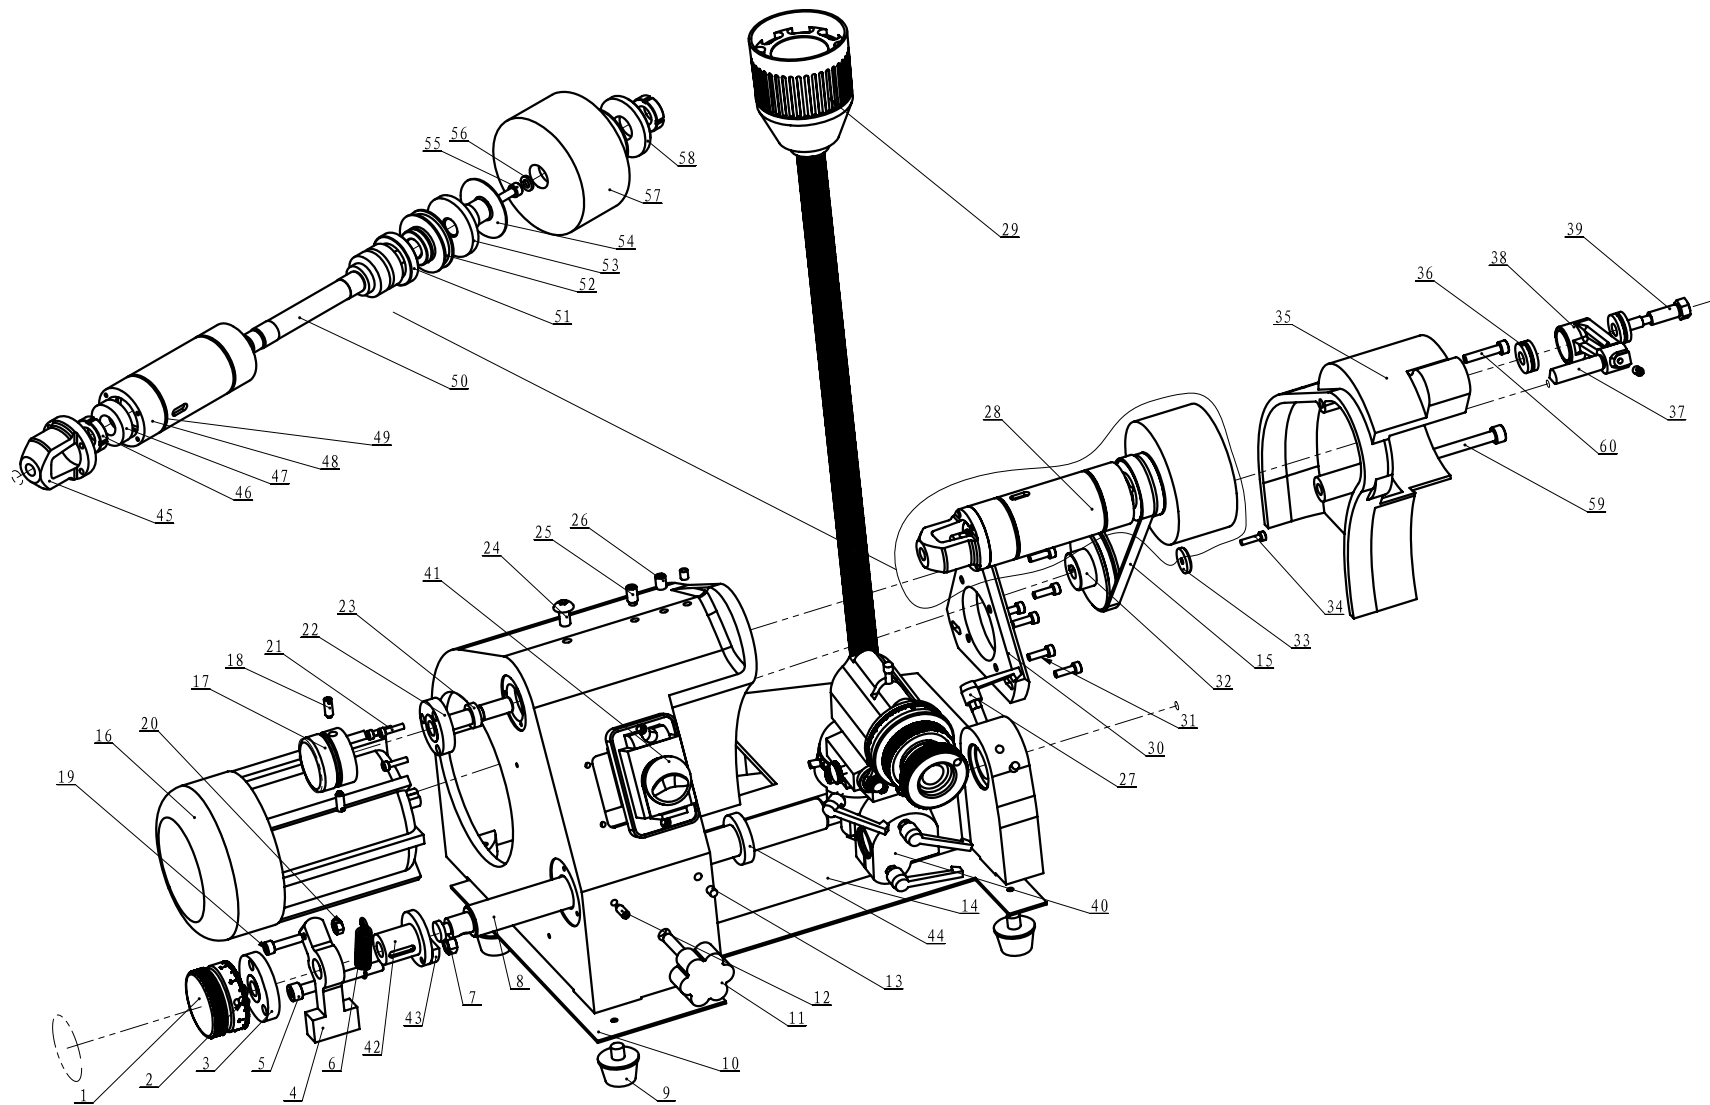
Ersatzteilzeichnung - Drawing spare parts 101-1008
